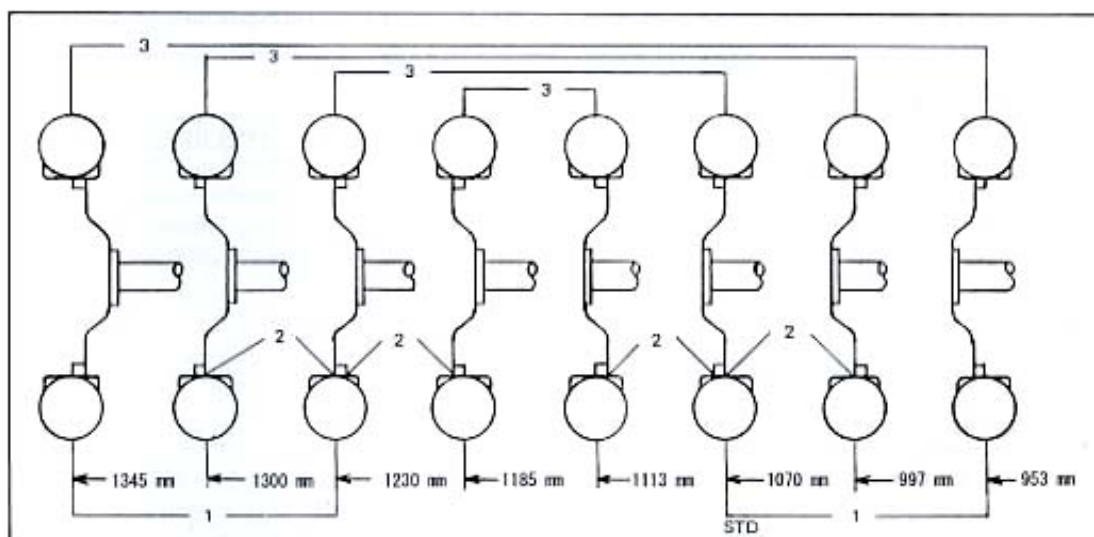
Ширина колеи задних колес (шины AG11.2-24 или 9.5-24)
